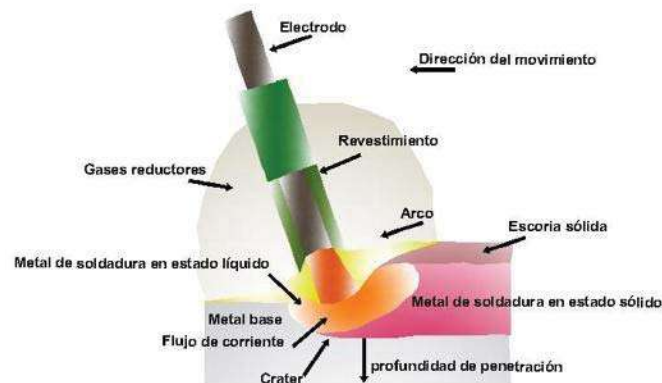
Soldadura de arco con electrodo revestido (SMAW).
